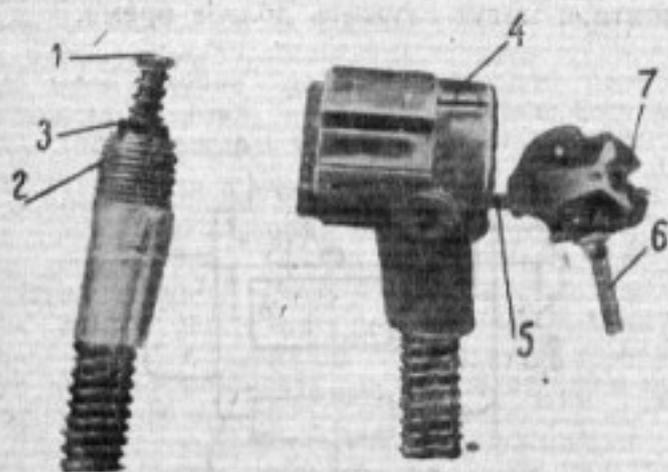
Концы бронированного провода: 1 — пружинный наконечник; 2 — втулка с резьбой для отвертывания корпуса прерывателя-распределителя; 3 — изоляция; 4 — корпус замка-выключателя зажигания; 5 — провод, заложенный в броне; 6 — клемма для соединения с бобиной; 7 — неподвижная пластинка замка-выключателя зажигания
